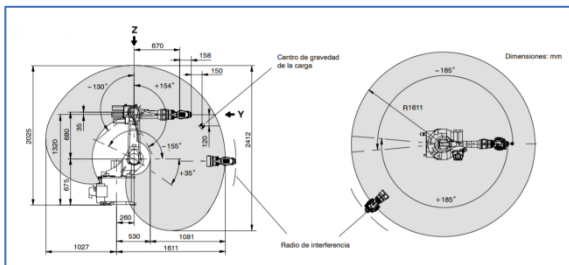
Diagrama de dimensiones en milímetros (mm).
